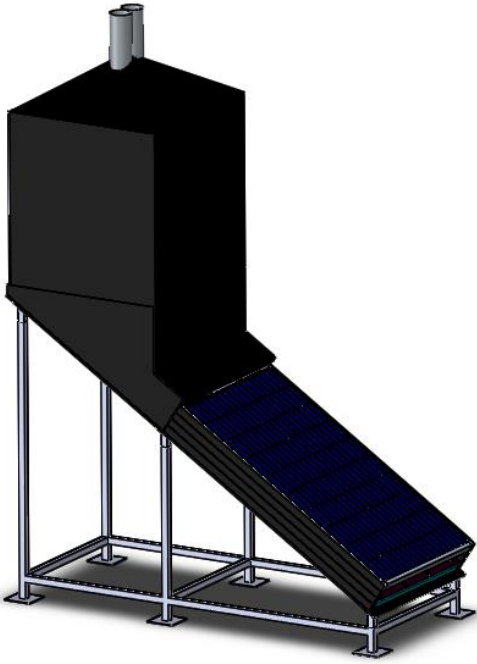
Conceito dimensionado em SolidWorks™ e o projeto final do secador solar.
